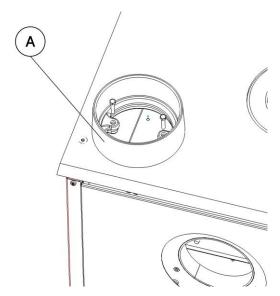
Colocamos a flange superior de saída de fumos.A
